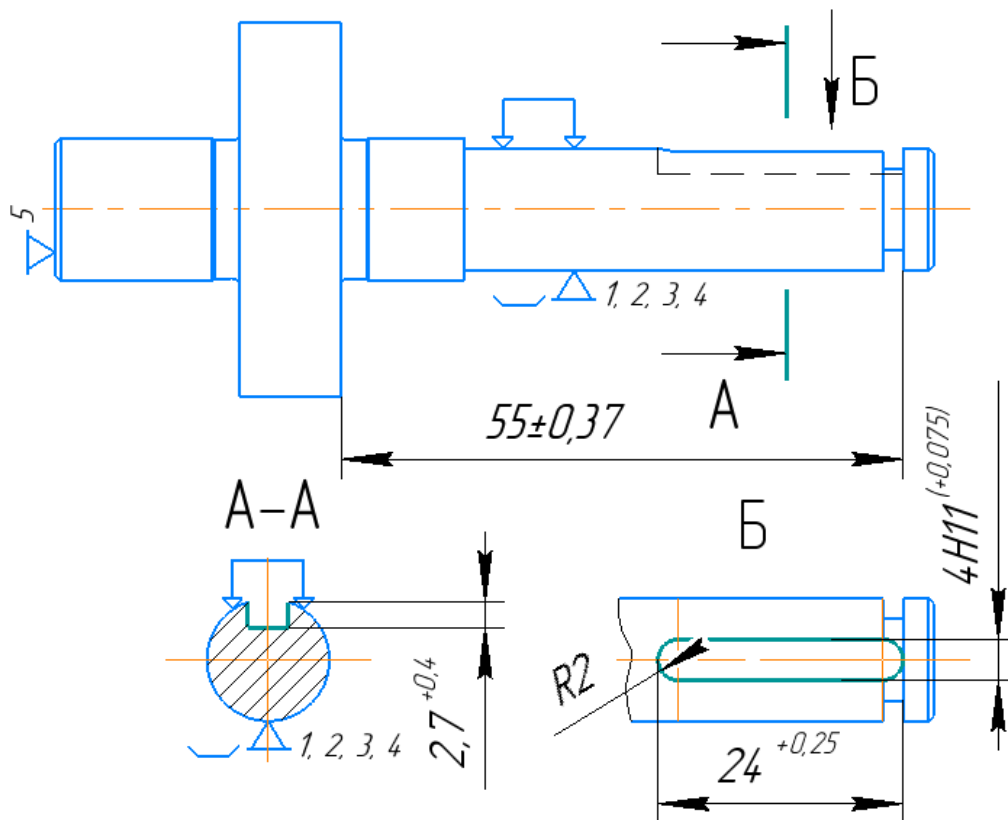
Базування заготовки 030 за схемою №2
